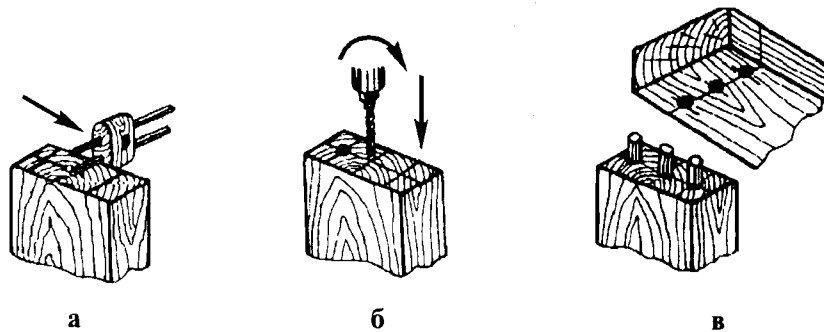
Последовательность сборки деталей шкантами: а — разметка торца; б — высверливание отверстий на торце; в — разметка, высверливание отверстий на пласти и соединение
